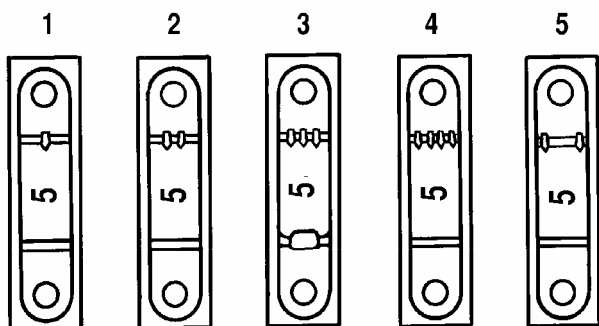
Метки на крышках коренных подшипников (счет опор ведется от передней части двигателя)
